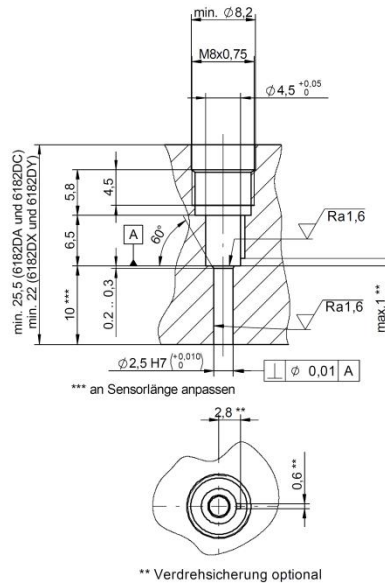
Montagebohrung für Einbau mit Montagemutter.
